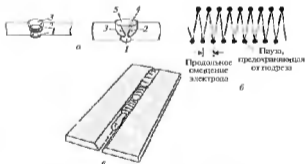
Сварка стыкового соединения со скосом кромок в нижнем положении: *а* — порядок наложения слоев, *б* — траектория движения электрода при выполнении последнего прохода; *в* — сварное соединение, 1—5 — номера слоев
